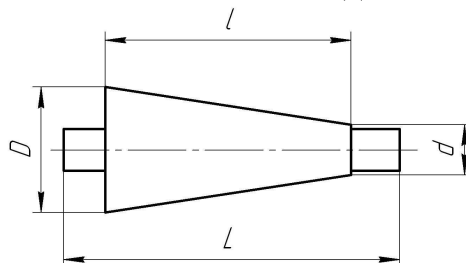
Схема расчета угла поворота салазок на угол конуса
